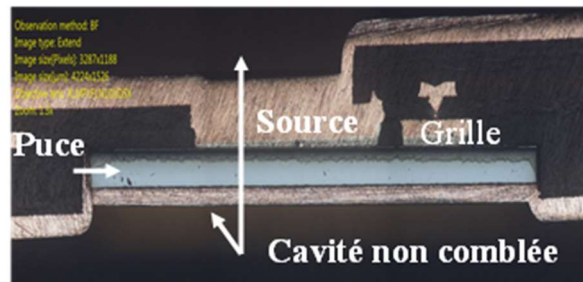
Coupe métallographique PCB de la cellule PNCBE
